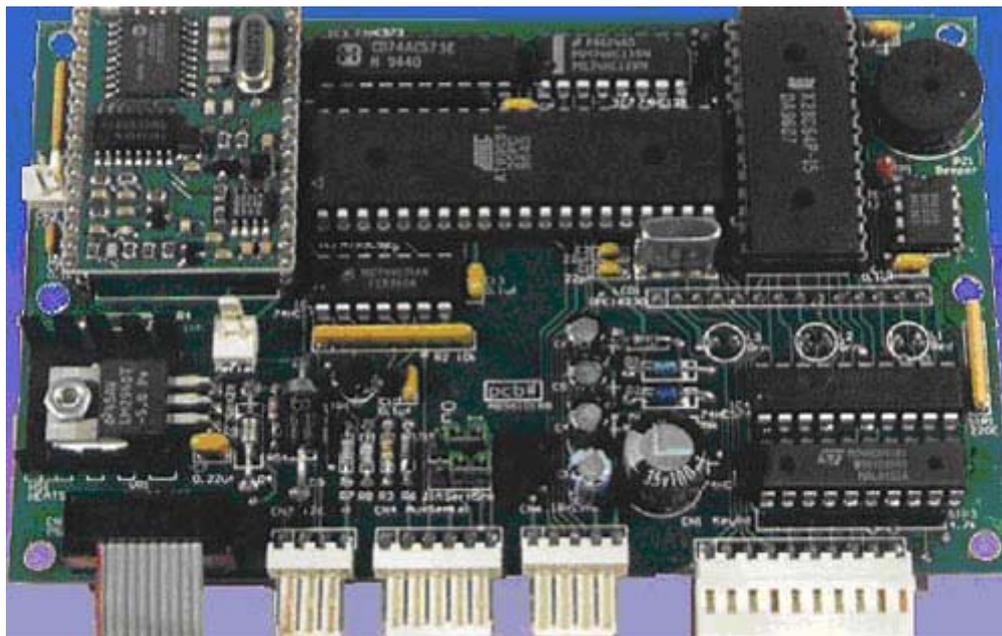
Placa de circuito impresso composta de componentes TH e SMT^[17]
